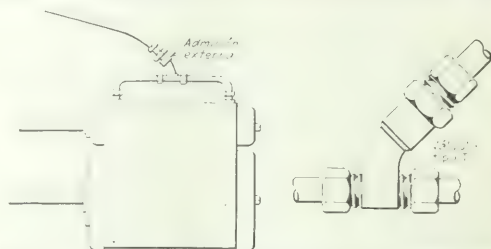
VÁLVULA EN EL TUBO LUBRICADOR. DETALLE DE LA VÁLVULA
